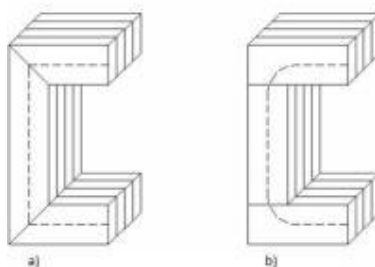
a) corte de chapas a 45° b) corte de chapas a 90° (SIEMENS,2006).
